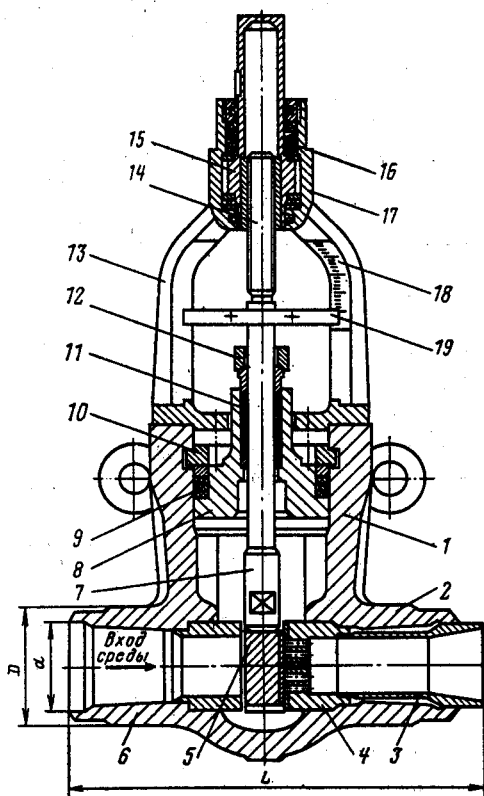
Клапан регулирующий и дроссельный шиберного типа D_y 100, 150 и 175. Серии 976, 992 и 993 — с защитной рубашкой; серия 977 — без защитной рубашки: 1 — корпус; 2, 6 — патрубок; 3 — защитная рубашка; 4 — профилированное седло; 5 — шибер; 7 — шток; 8 — бесфланцевая крышка; 9 — сальниковое уплотнение; 10 — разъемное кольцо; 11 — сальниковое уплотнение штока; 12 — нажимная планка; 13 — бугель; 14 — ходовой винт; 15 — ходовая гайка; 16 — подшипниковая опора; 17 — головка; 18 — шкала; 19 — указатель положения затвора
